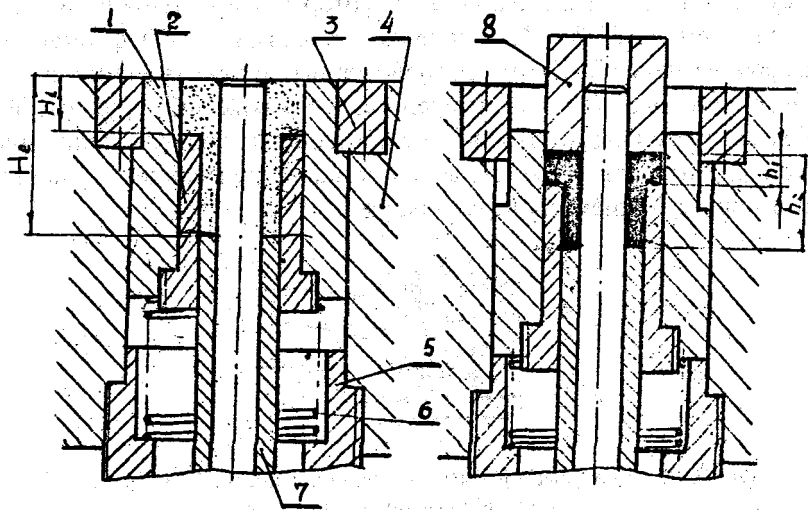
Схема пресс-формы для прессования втулок с наружным верхним буртом: 1 – матрица; 2; 7 – составные элементы нижнего пуансона; 3 – кольцо; 4 – обойма; 5 – упор; 6 – пружина; 8 – верхний пуансон
